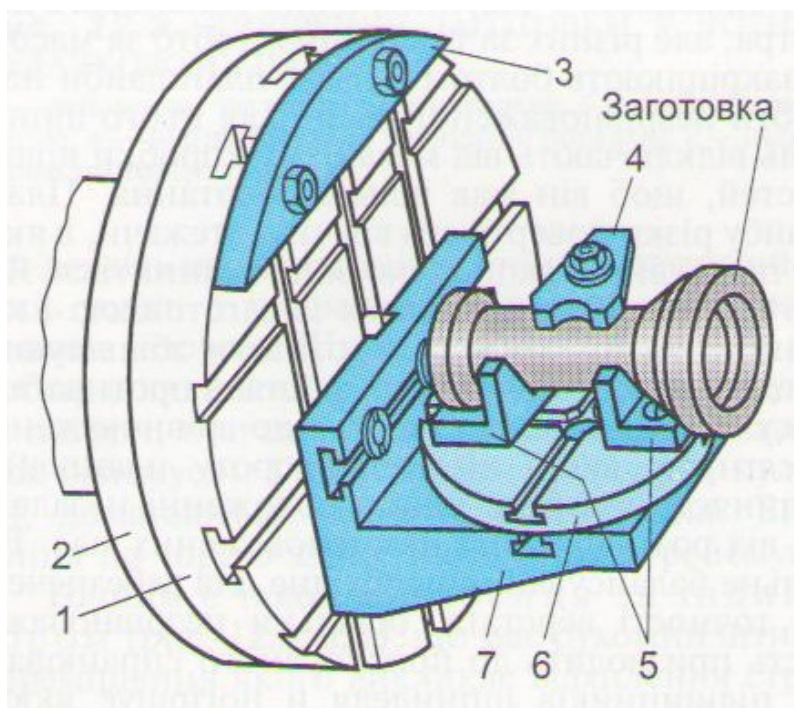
Токарний пристрій-«косинець», складений з деталей комплексу УСП:
